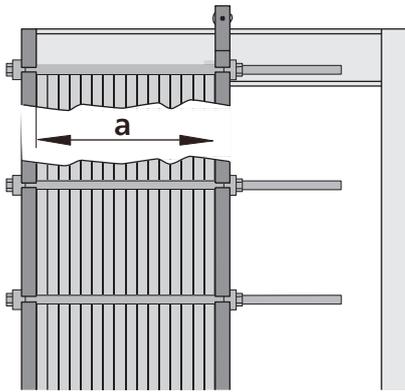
d – Mesure de la cote de serrage entre la plaque fixe et la plaque mobile
